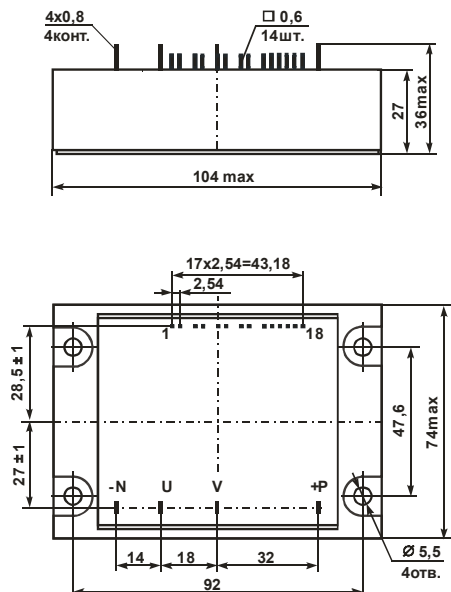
Габаритный чертеж модулей M13B-10-6(12)
